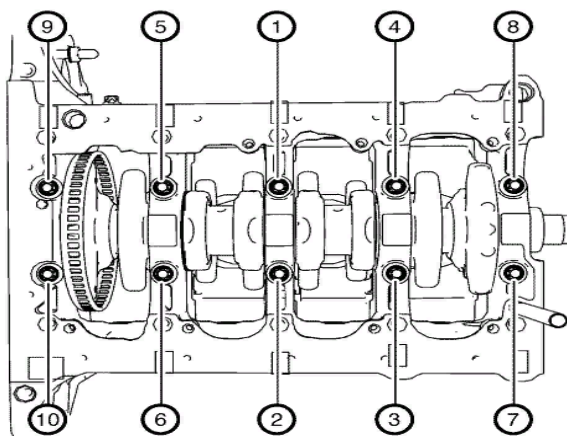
Схема затяжки гаек коренных подшипников ДВС
